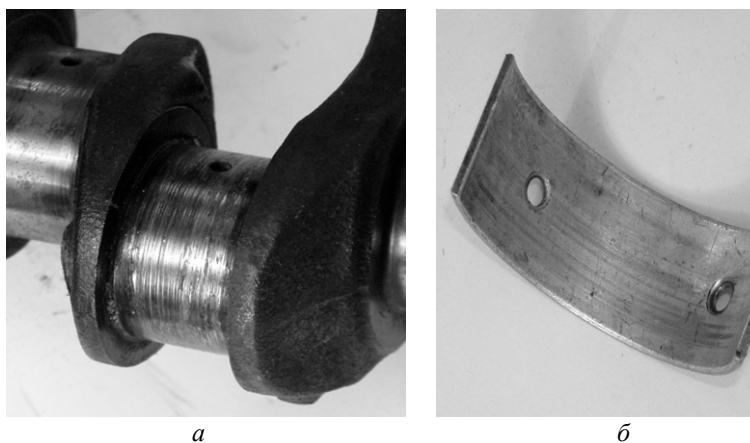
Шейка и вкладыш коленчатого вала со следами задира
